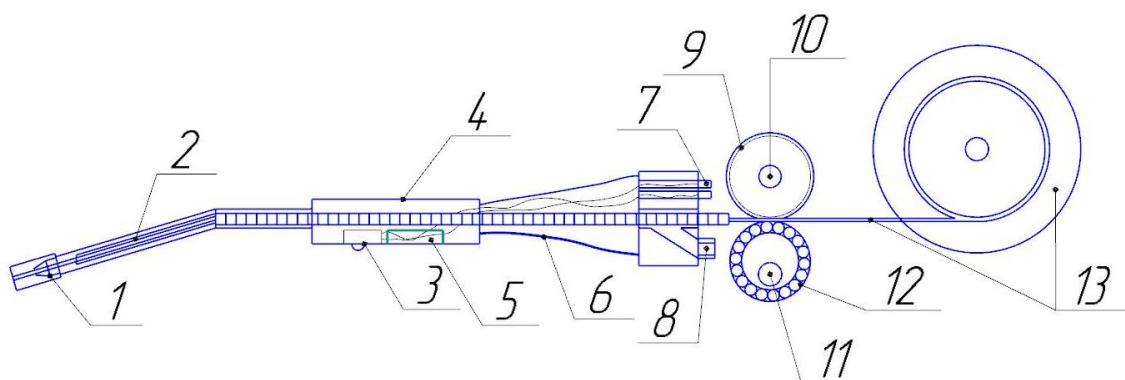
Эскиз модифицированной сварочной горелки: 1 - медная (латунная) направляющая проволоки; 2 - спиральная металлическая "рубашка"; 3 - кнопка "Пуск"; 4 – рукоять; 5 – элемент управления (кнопка или датчик); 6 – шланг; 7 - контакты кнопки; 8 - газовый штуцер; 9 – проточка; 10 - ось двигателя; 11 - эксцентрическая ось; 12 – подшипник; 13 - проволока и бобина.
